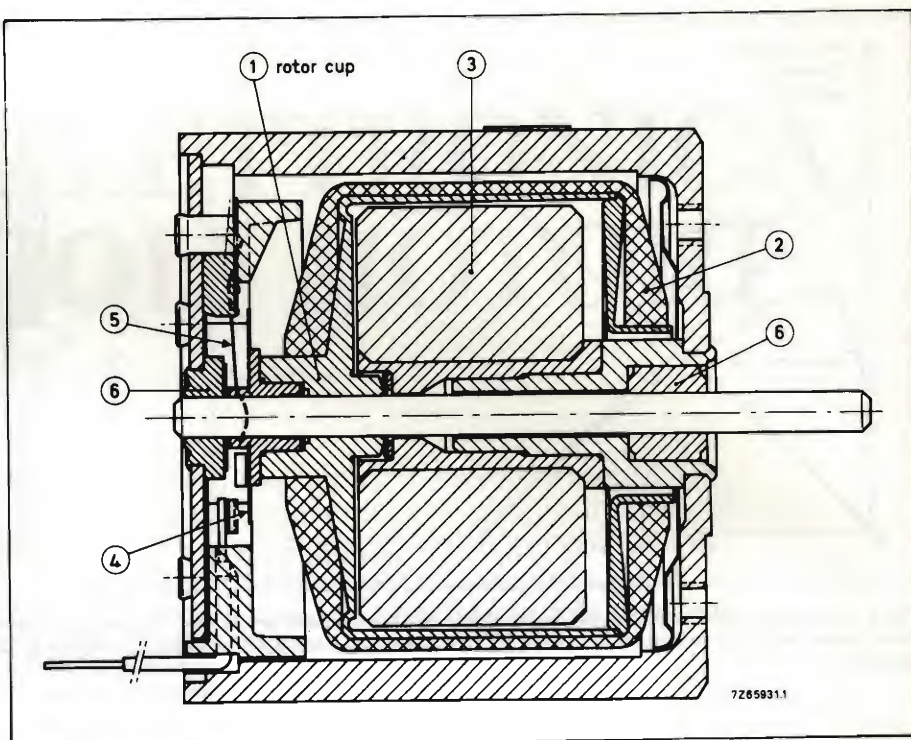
Struttura interna di un motore con rotore senza ferro: 1 = rotore; 2 = avvolgimento del rotore; 3 = magneti dello statore; 4 = commutatore; 5 = spazzole; 6 = bocche.
